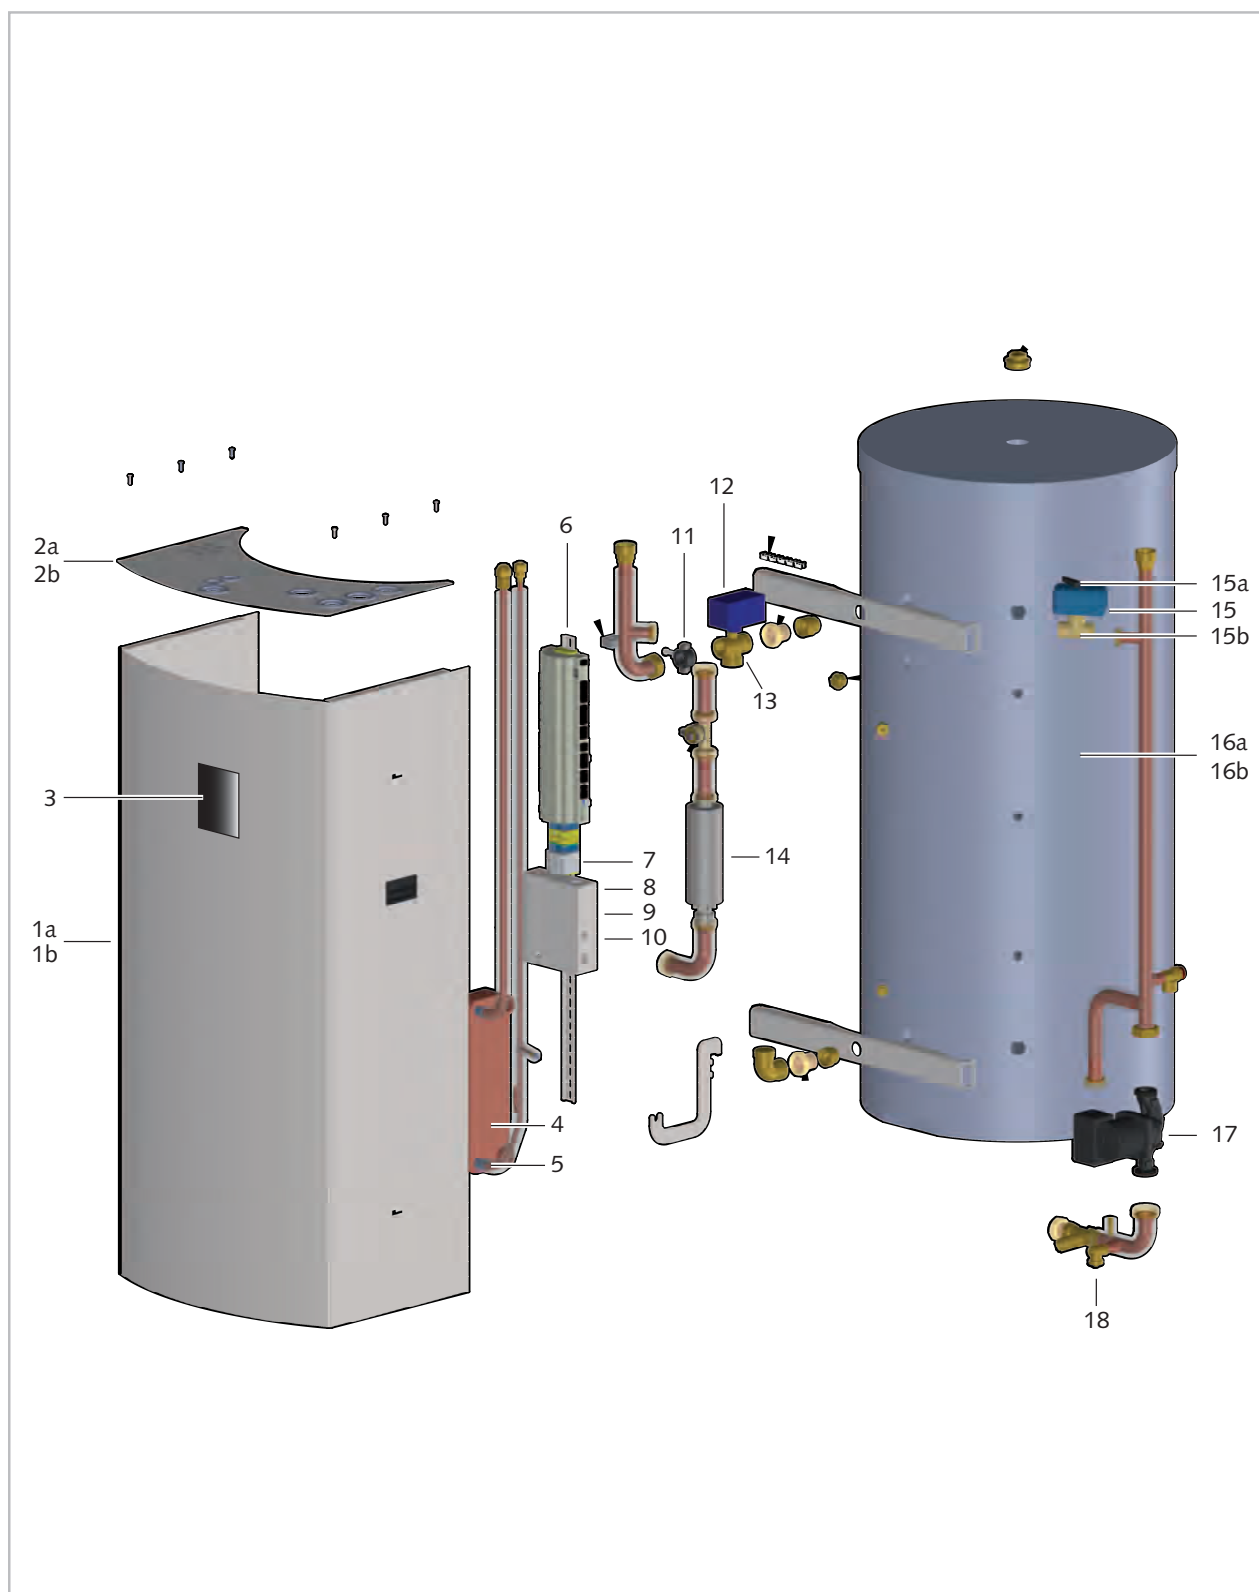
Explosionszeichnung Innenmodul WKF NEO compact
